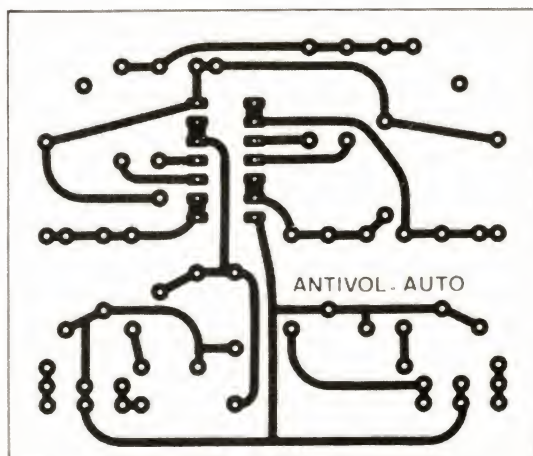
Dessin du circuit imprimé, côté cuivre, échelle 1.
